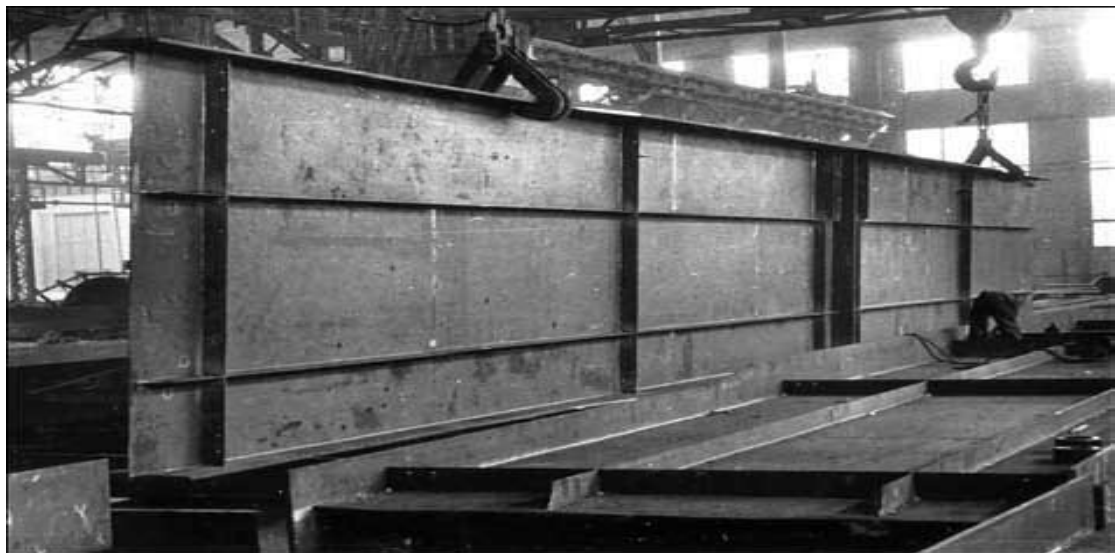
Сварка трактором ТС-17-М стыкового шва стенки
